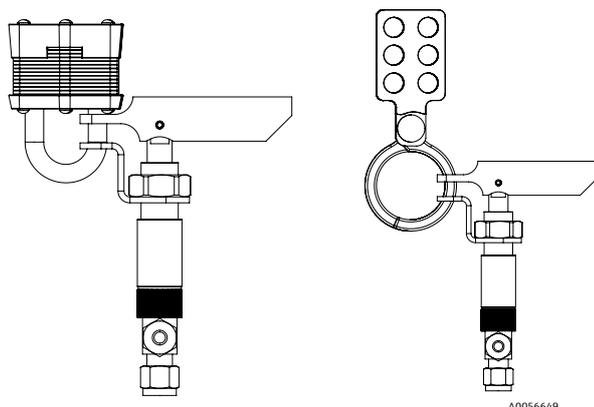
Блокировка / маркировка газоанализатора JT33 типа TDLAS
